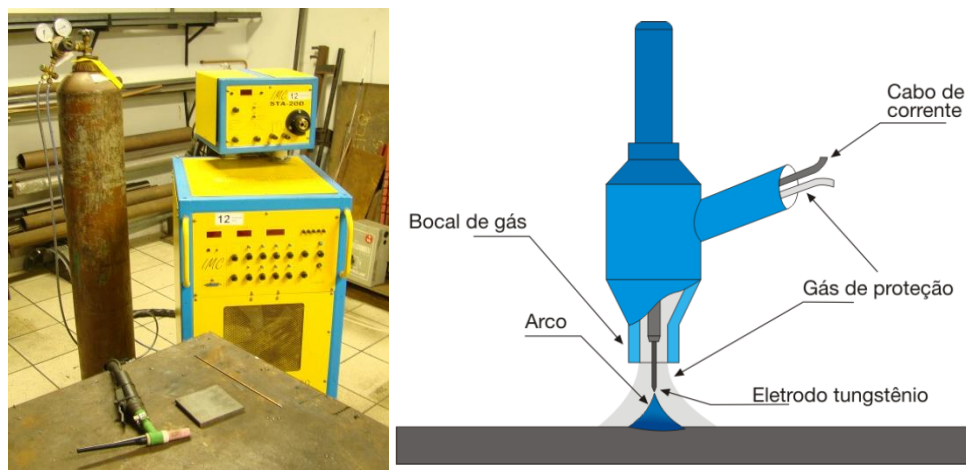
Bancada de trabalho TIG e detalhe da tocha de soldagem
